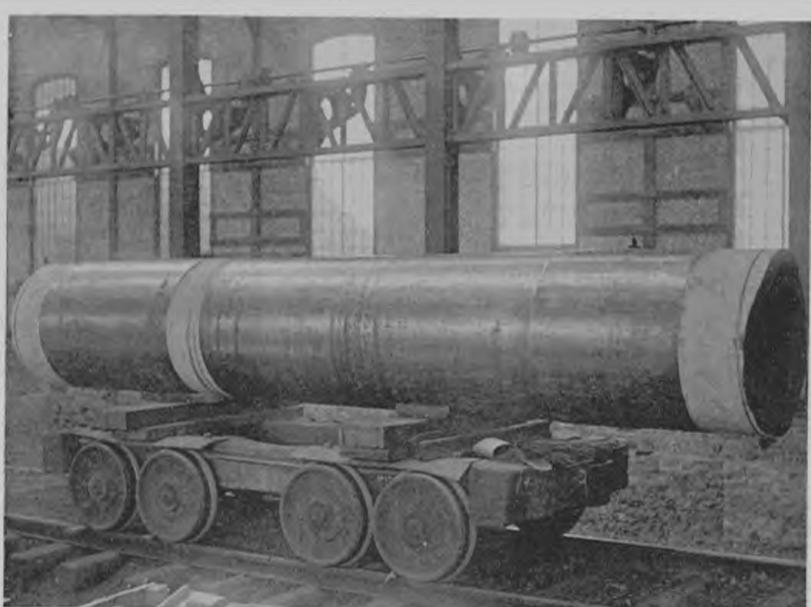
VUE DE LA JAQUETTE DU CANON DE 330 m/m, 2
